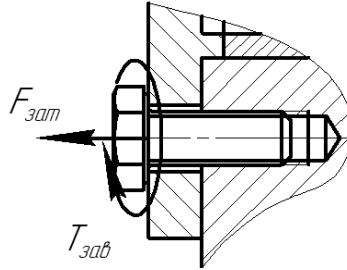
Соединение крышки подшипника с корпусом
